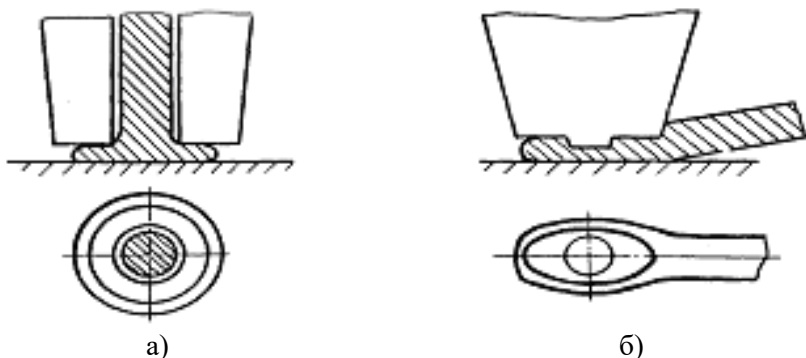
Основные виды термокомпрессионных соединений: а – соединение встык (термокомпрессия капилляром с образованием шарика); б – сварка внахлестку инструментом с канавкой на торце
